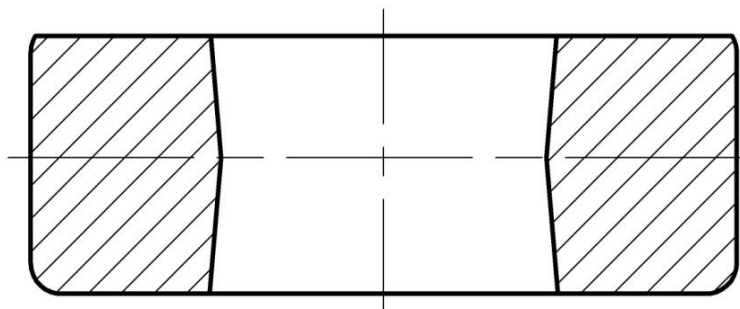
Ескіз заготовки деталі «Сателіт»
